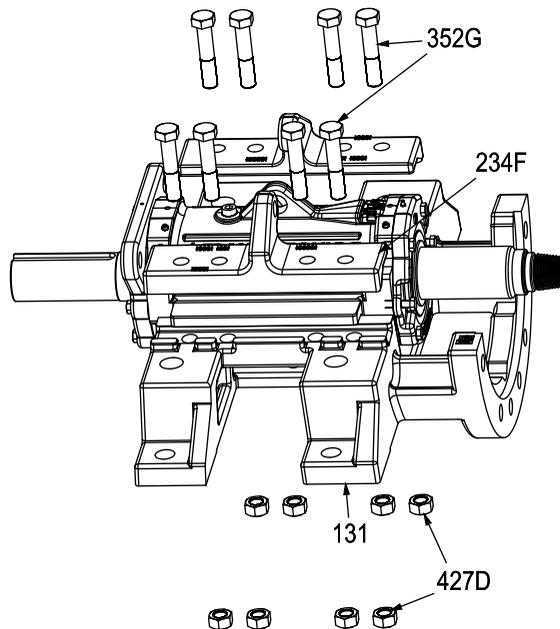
Pré-assemblage du boulonnage de la plaque de réglage de bâti
